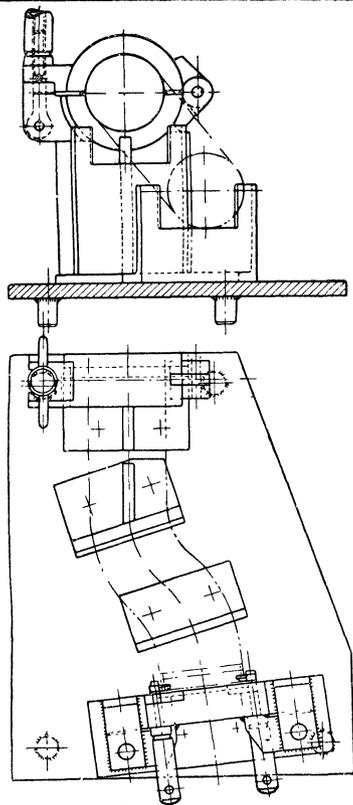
Приспособление для сборки и прихватки всасывающего патрубка.
